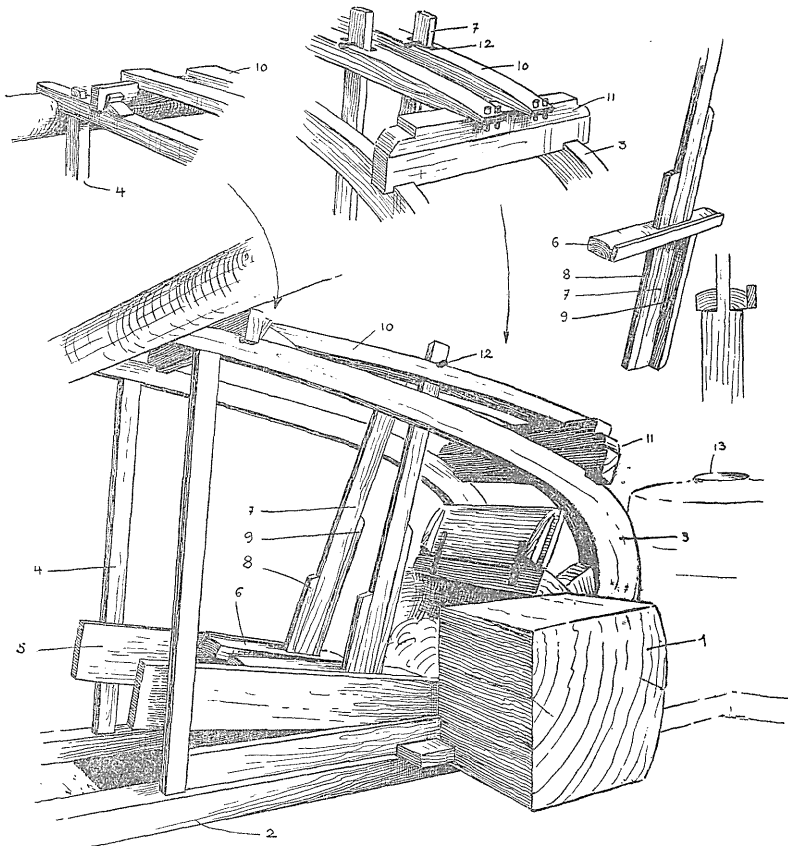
Pisão de Fonte Branca (Castro Daire)
